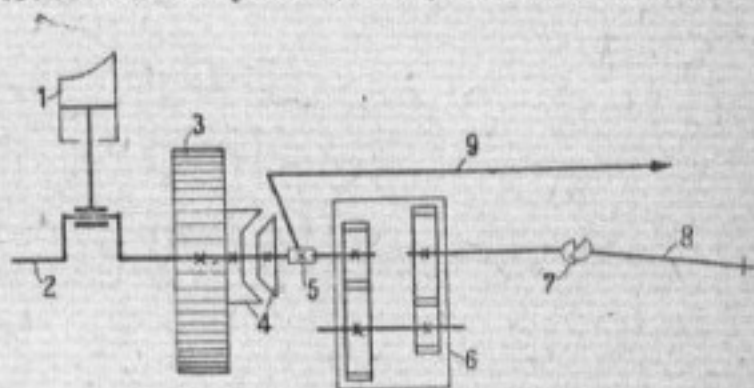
Кинематическая схема автостартера. 1 — поршень двигателя ЛД-3; 2 — коленчатый вал; 3 — маховик; 4 — конусное фрикционное сцепление; 5 — шлицевая муфта; 6 — редуктор; 7 — карданное сочленение; 8 — приводной вал; 9 — тяга рукоятки включения
